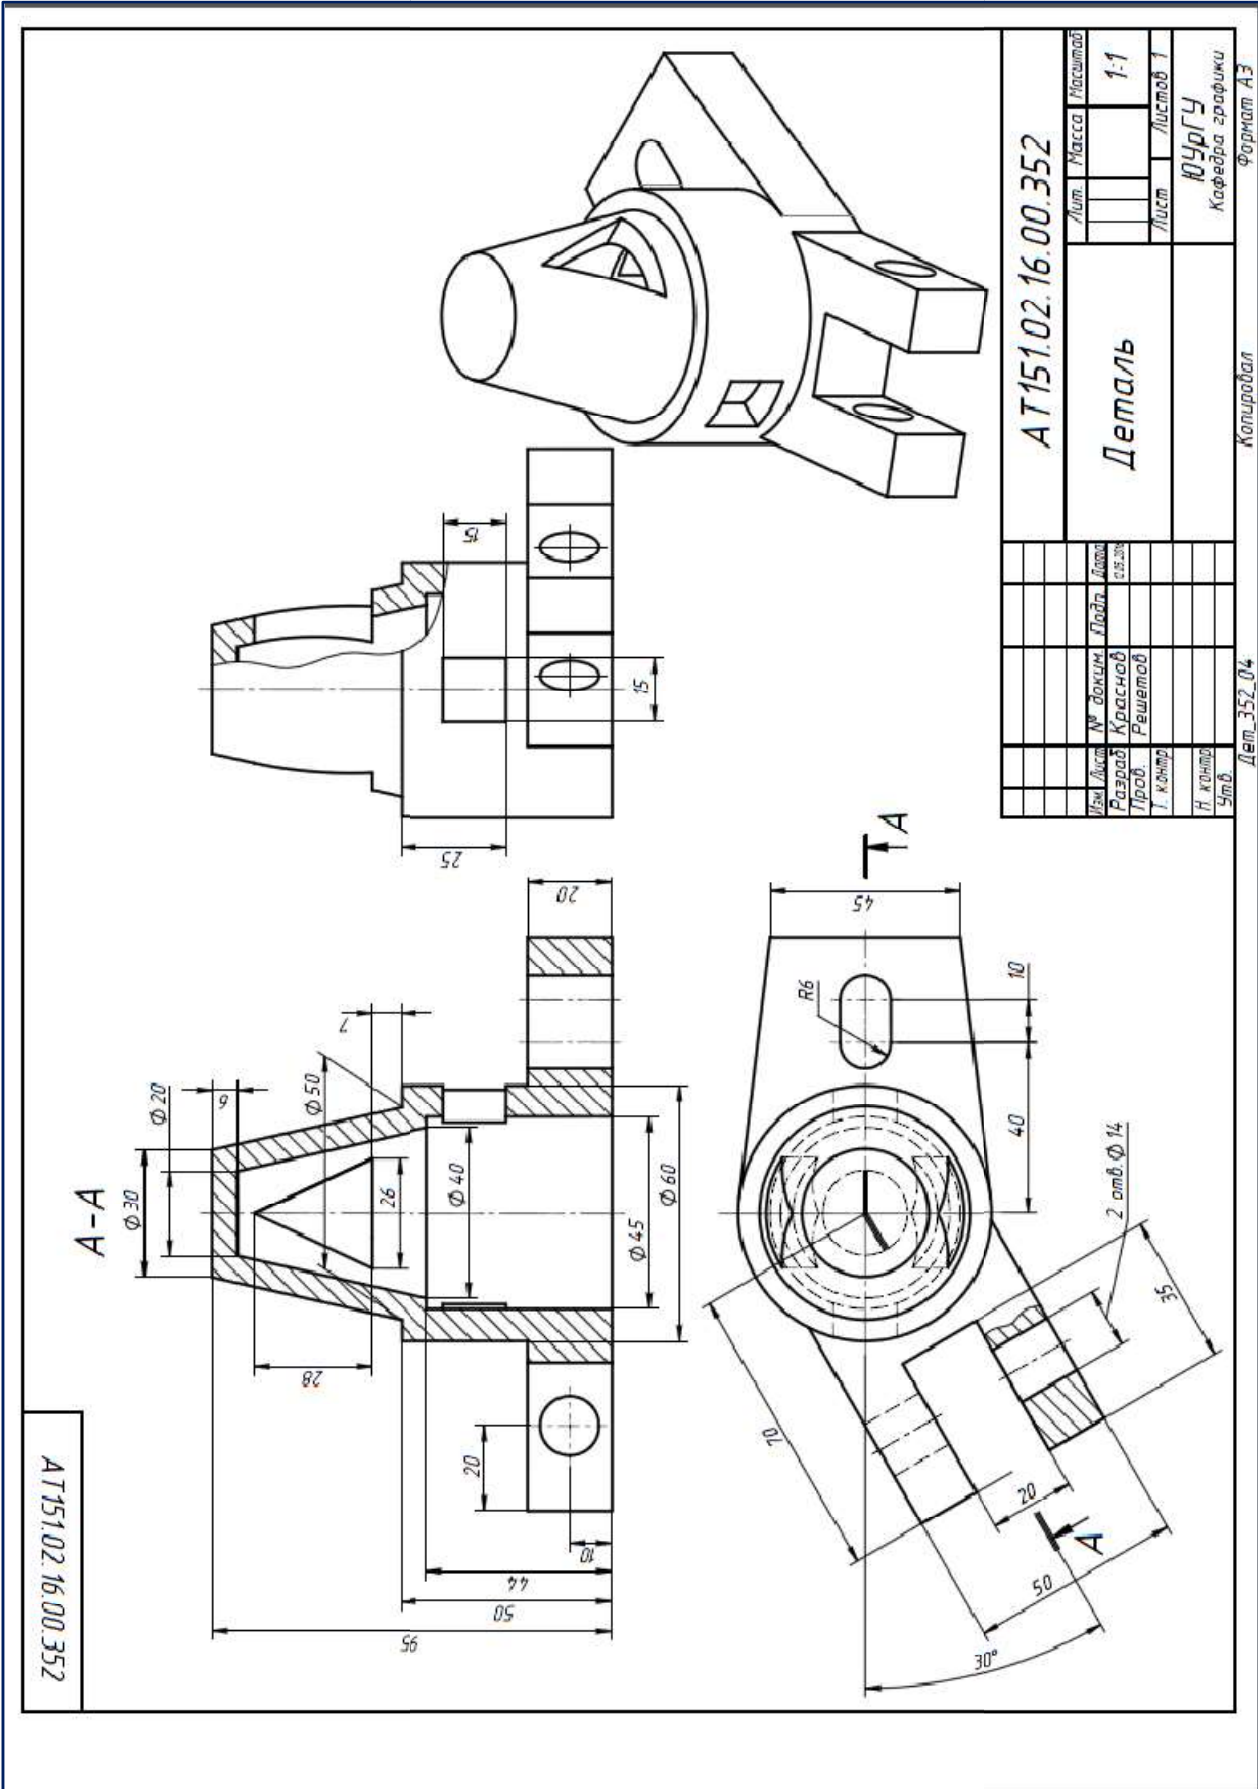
Чертеж детали сохранённый в формате *.pdf
